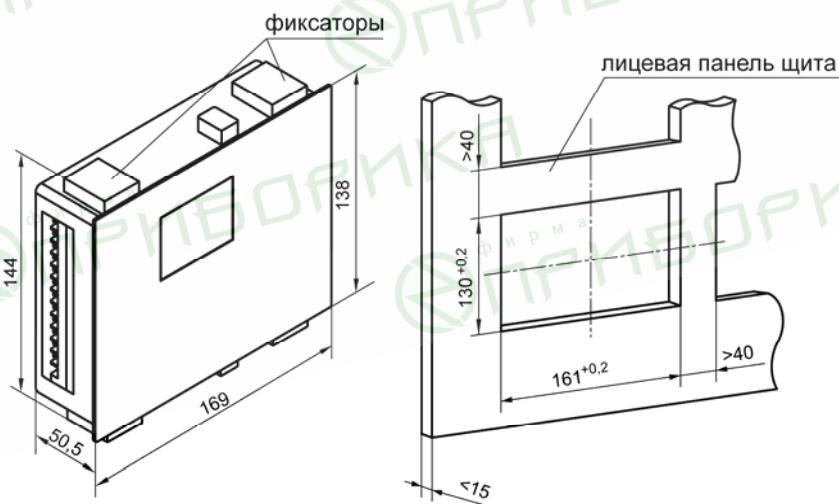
Габаритный чертеж прибора в корпусе Щ
